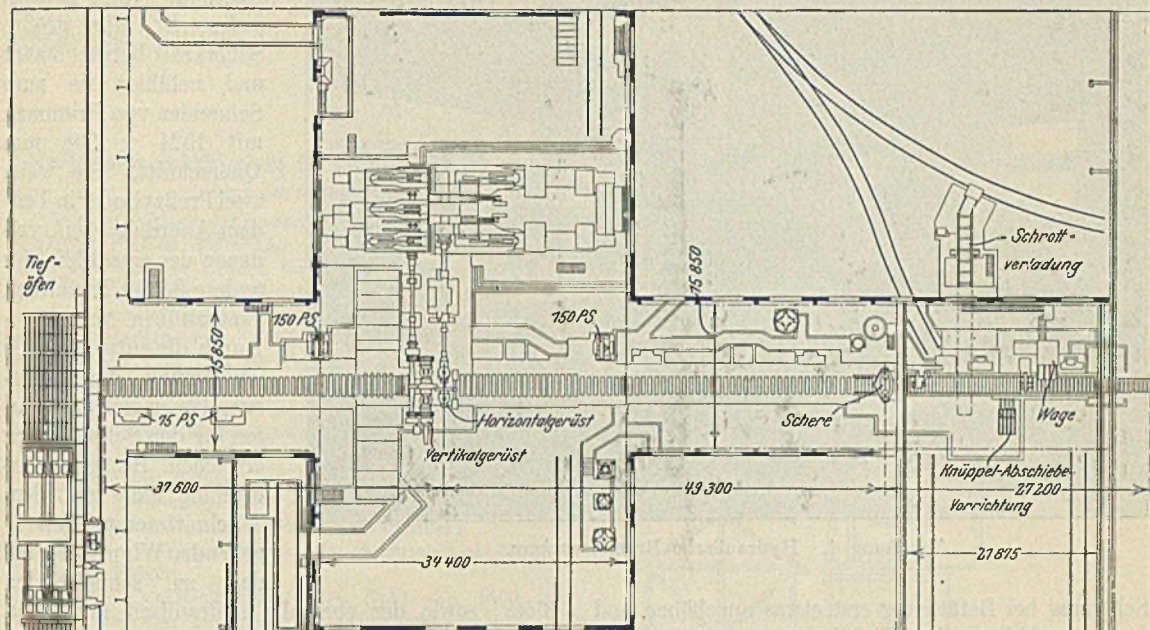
Grundriß des Brammen-Universal-Walzwerkes in Gary.
